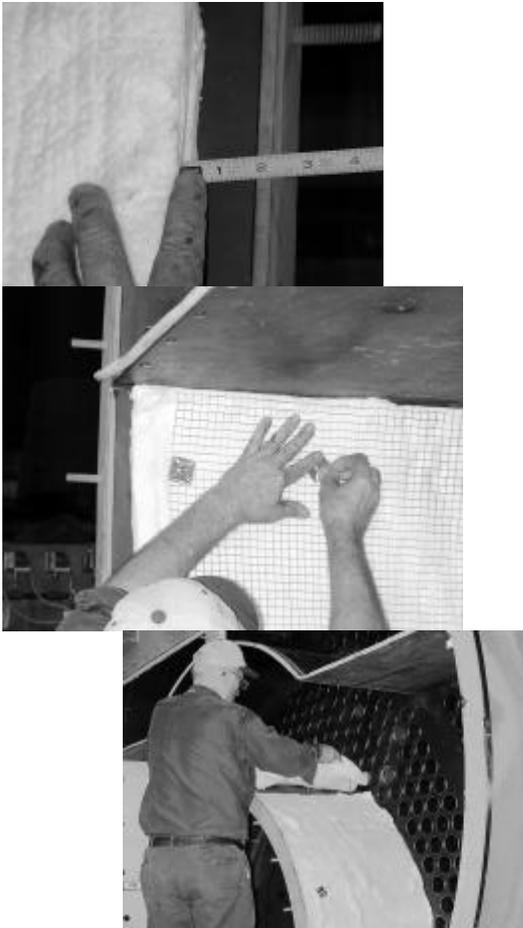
Corte el aislante, ponga la malla metálica, y ponga en su lugar
